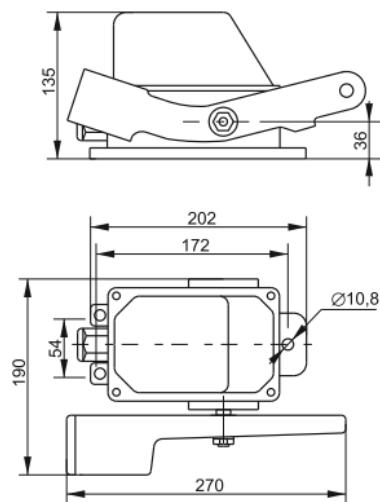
Габаритные и установочные размеры выключателей КУ-703 У1
